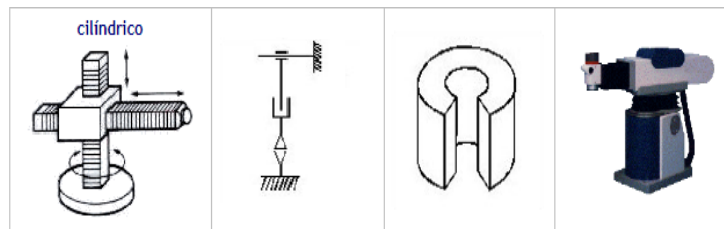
Geometría de una estructura mecánica para un manipulador Cilíndrico.
